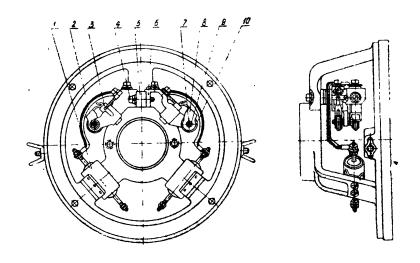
Щит подшипниковый со стороны контактных колец: 1 — проходной кондейсатор; 2 — гайка оси нажимной пружины; 3 — щетка; 4 — винты, крепящие щеткодержатели к пальцу; 5 — палец щеткодержателя; 6 — щеткодержатель; 7 — ось нажимной пружины; 8 — нажимной палец; 9 — пружинное кольцо; 10 — пружина.
